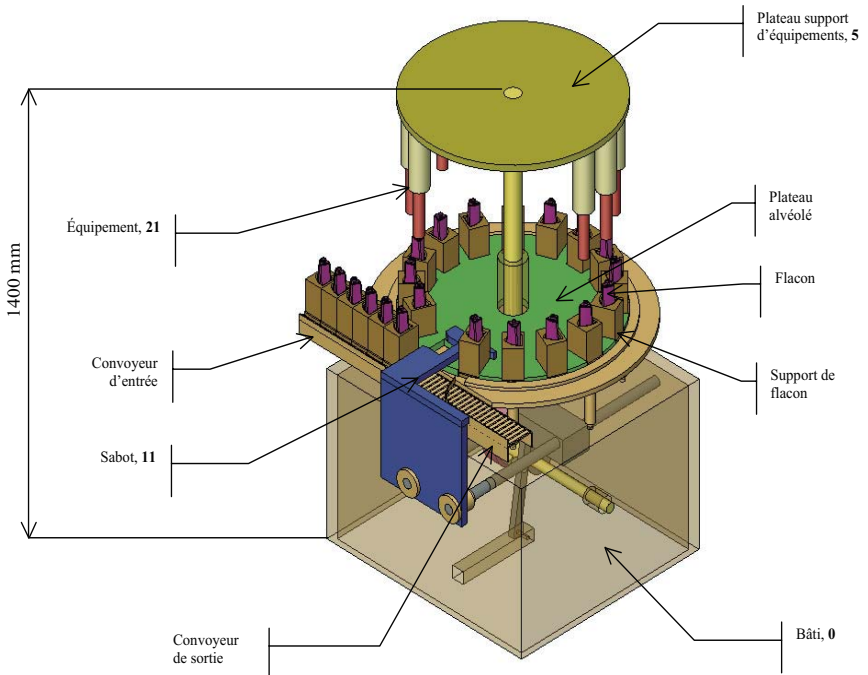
b Vue de dessus de la machine de remplissage-sertissage
